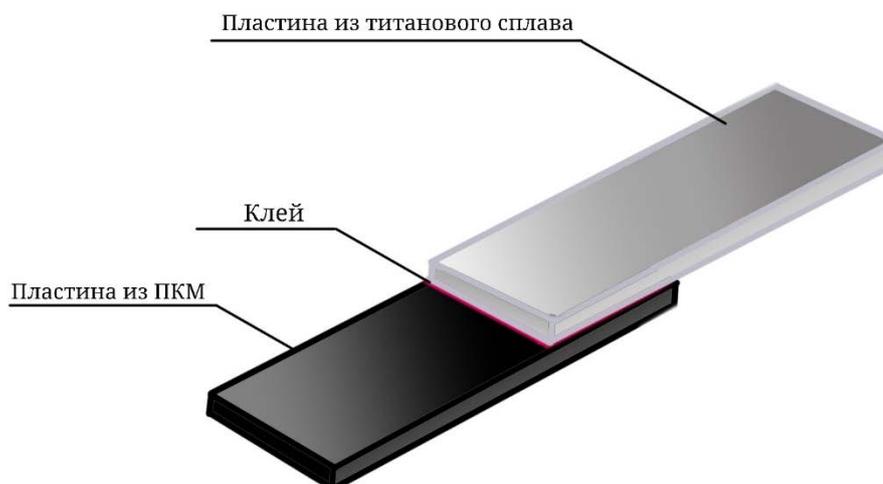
Образец для испытаний на сдвиг клеевого соединения
